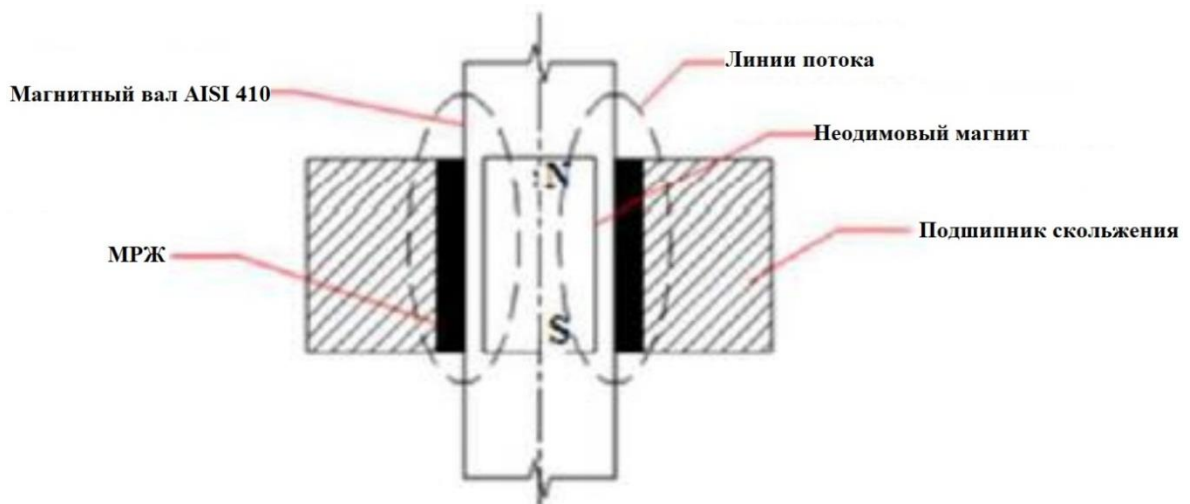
Конструкция подшипника скольжения [152]
